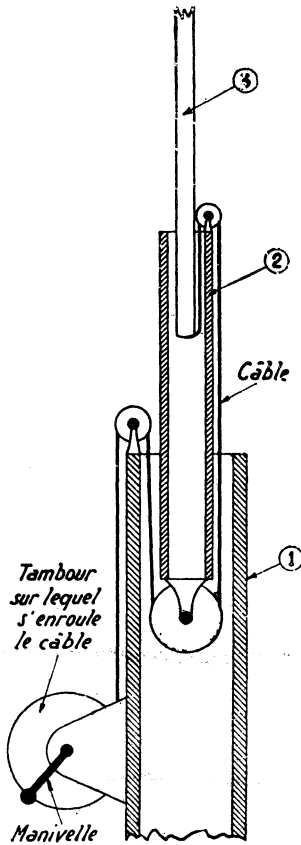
Principe du mât télescopique. Mât formé de trois tubes.
